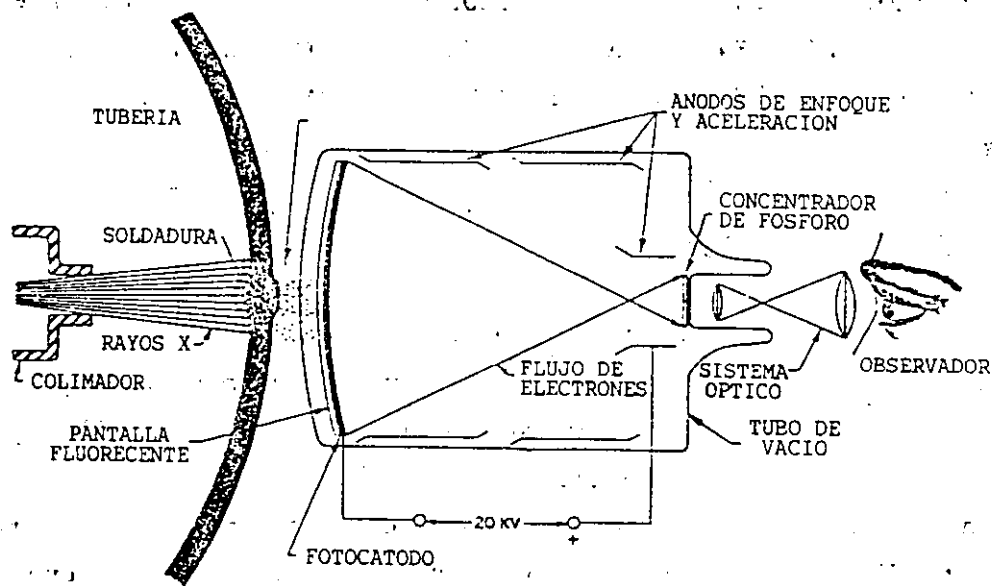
FIG. EXPLICACION DIAGRAMATICA DE UNA EXAMINACION FLUOROSCOPICA A UNA SOLDADURA DE TUBERIA.
